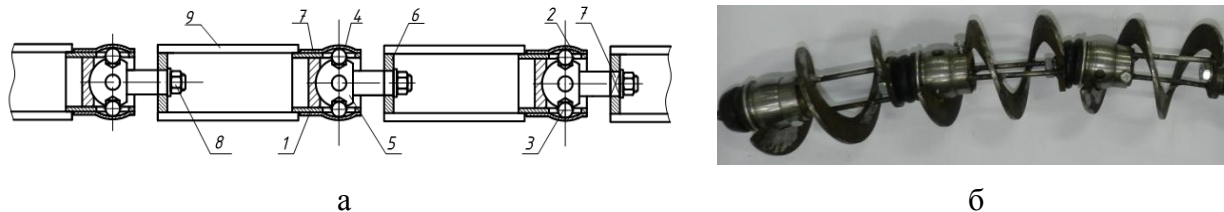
Конструктивна схема (а) та загальний вигляд (б) гвинтового секційного шарнірного робочого органу для транспортування зерна
